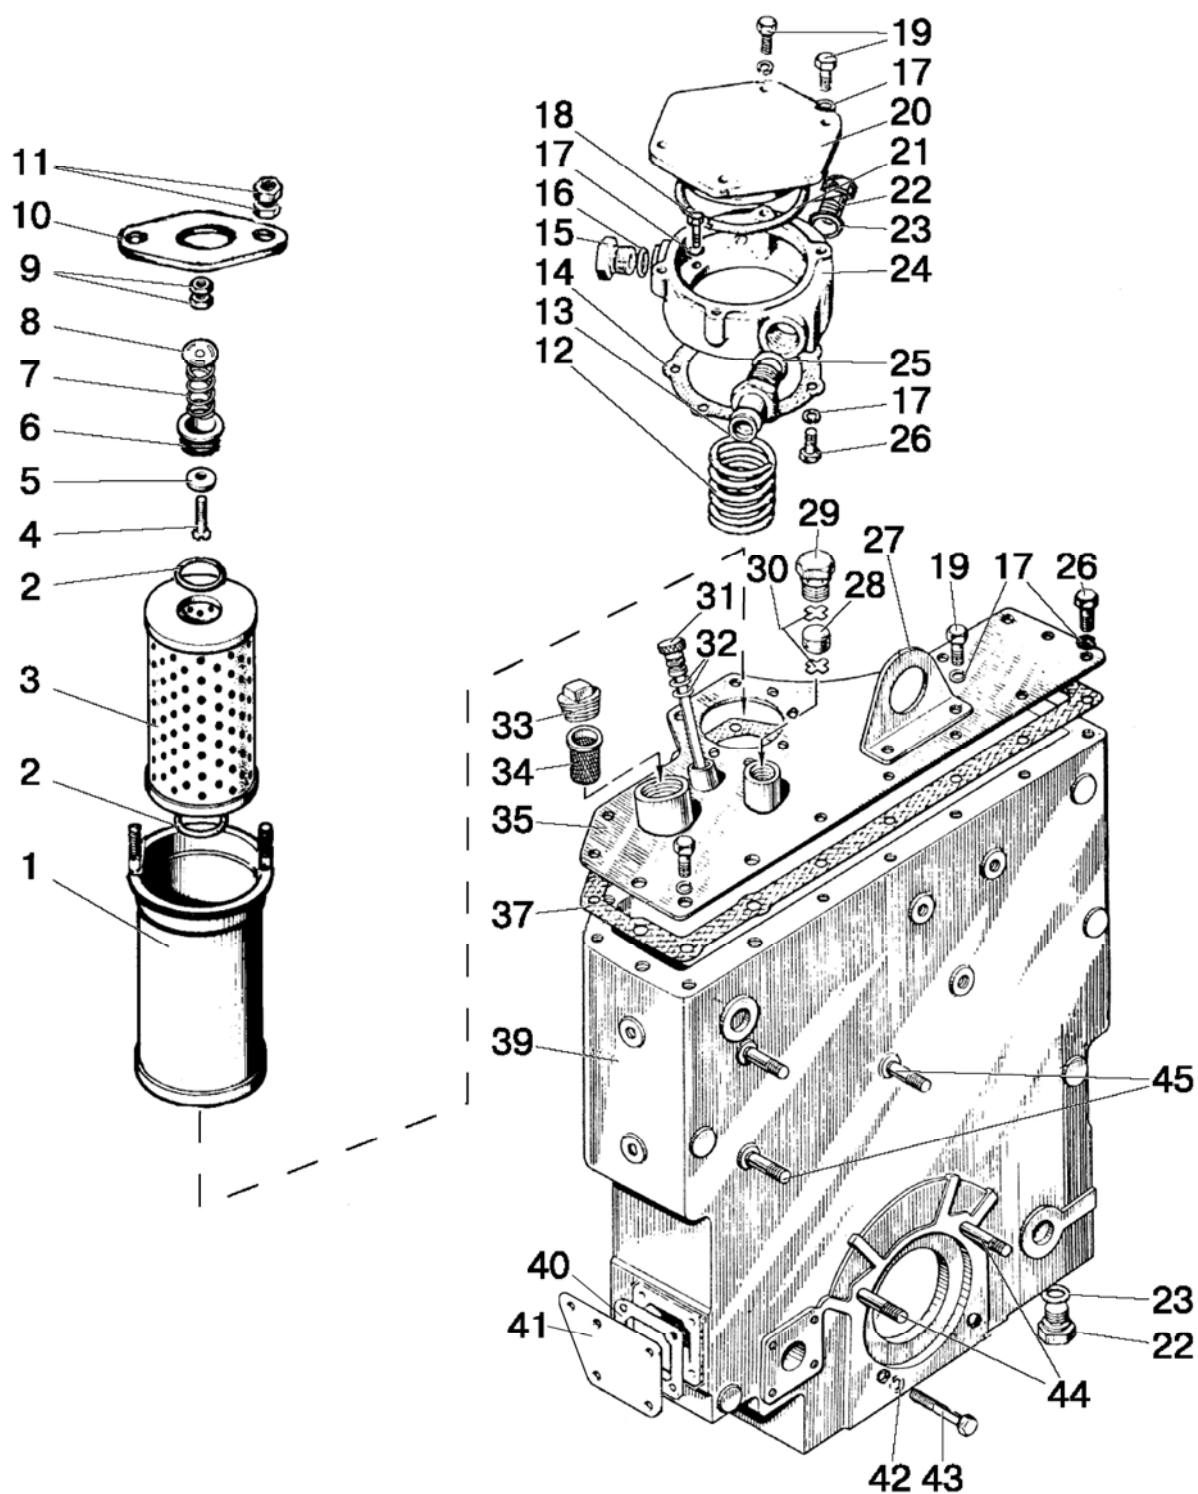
Корпус гидроагрегатов и фильтр. Вариант
